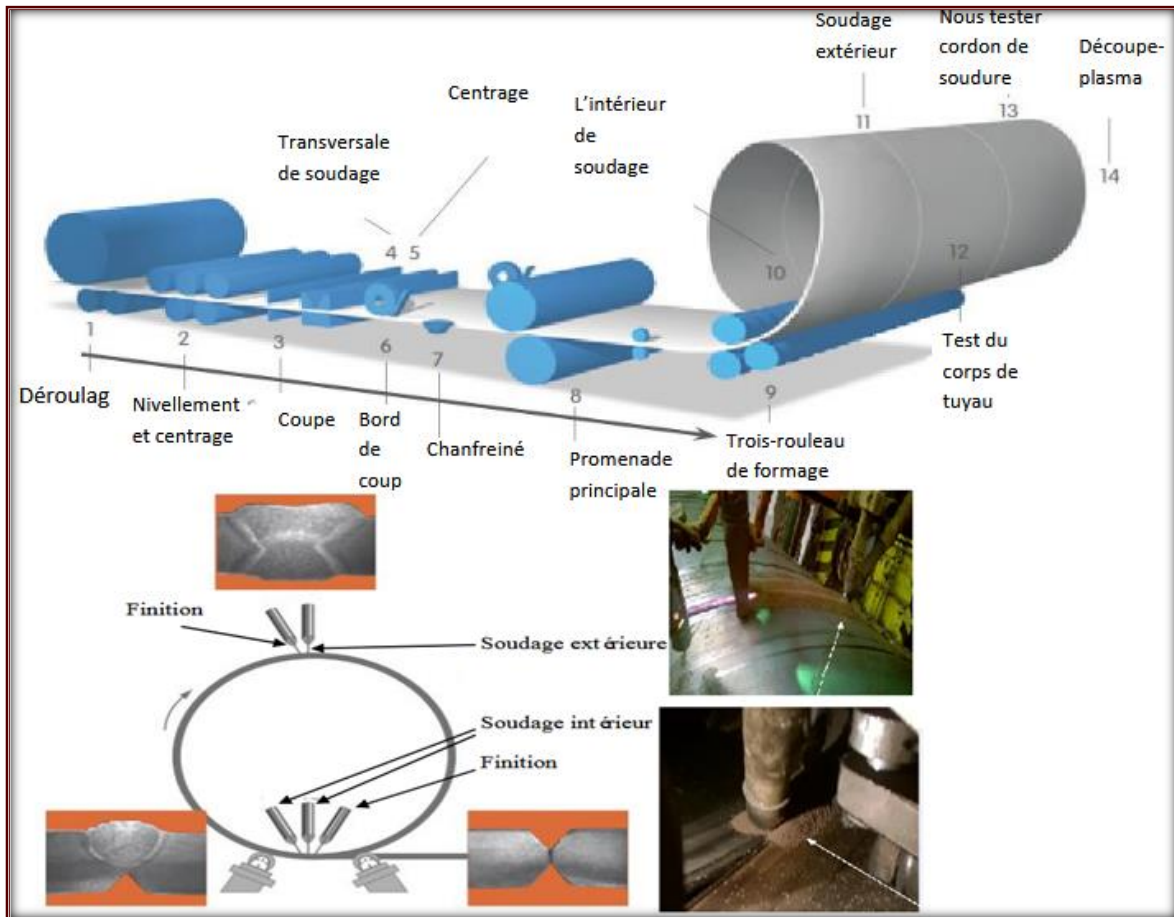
Technique de fabrication des tubes soudés en spirale [21].
